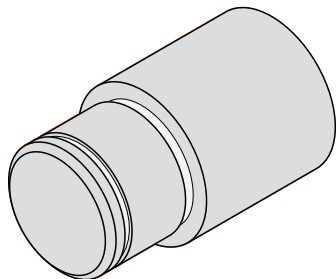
Образцовая деталь – Чистовая обработка внешнего контура
